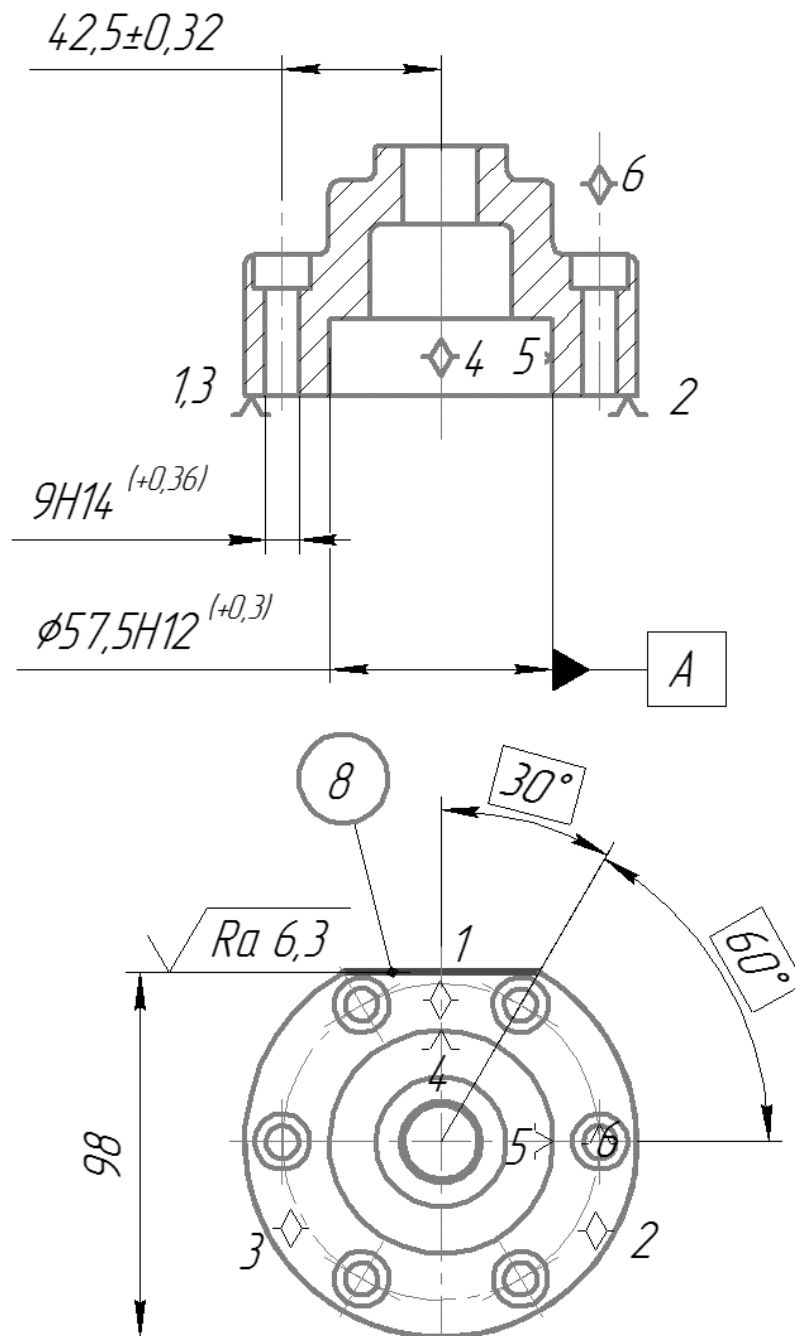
Эскиз детали «Крышка» на фрезерной операции
